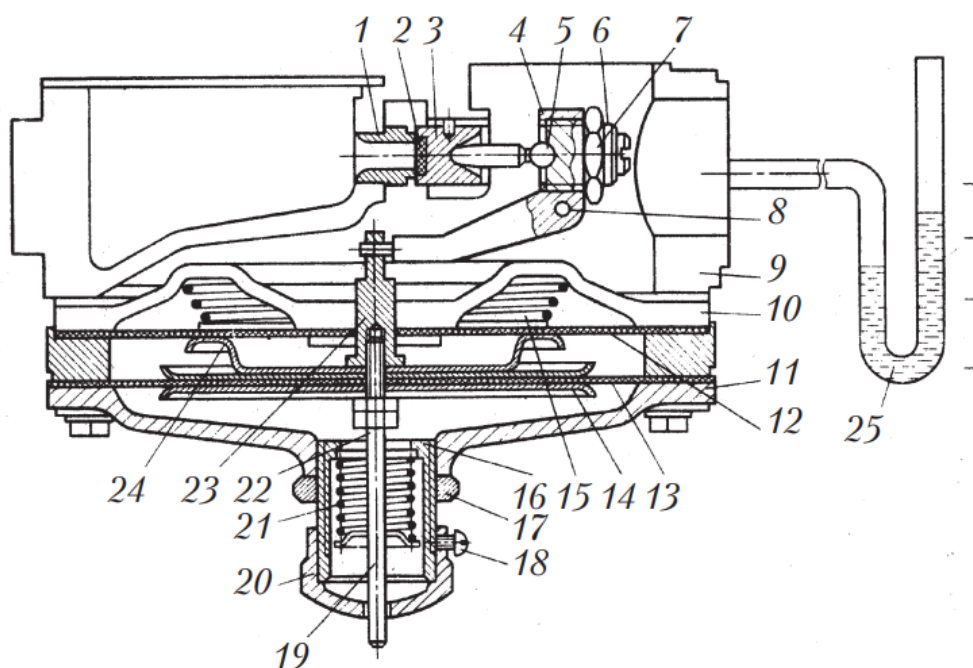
Схема второй ступени РНД: 1 — седло клапана; 2 — уплотнитель; 3 — клапан второй ступени; 4 — рычаг; 5 — толкатель клапана; 6, 18 — регулировочные винты; 7, 17 — контргайки; 8 — ось; 9, 10 — корпуса; 11, 20 — крышки; 12, 13 — мембраны; 14 — усилительный диск; 15, 21 — пружины; 16 — регулировочный ниппель; 19 — штифт; 22 — стержень; 23 — шток; 24 — упор мембраны; 25 — вакуумметр
